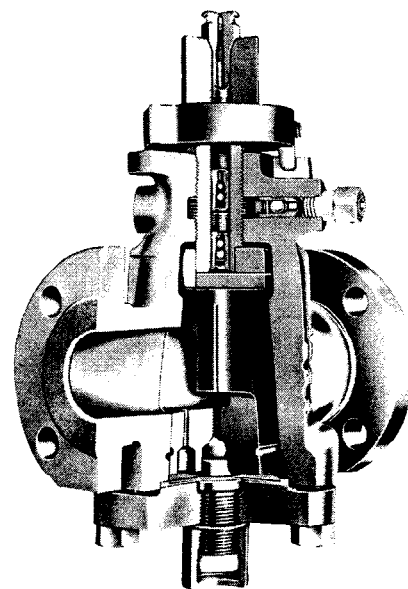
Válvula de macho lubricada; tapa inferior atornillada
